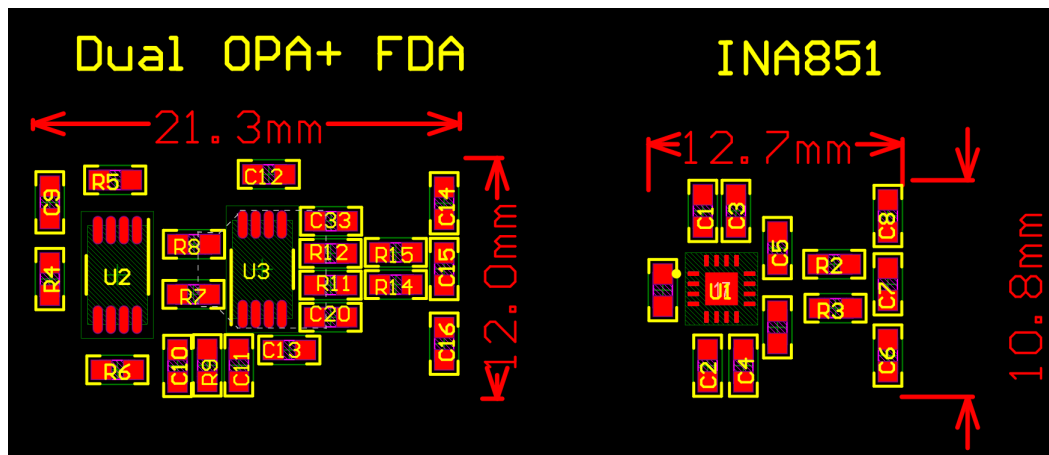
估算的 PCB 面积，INA851 与 OPA2210-THP210 对比
